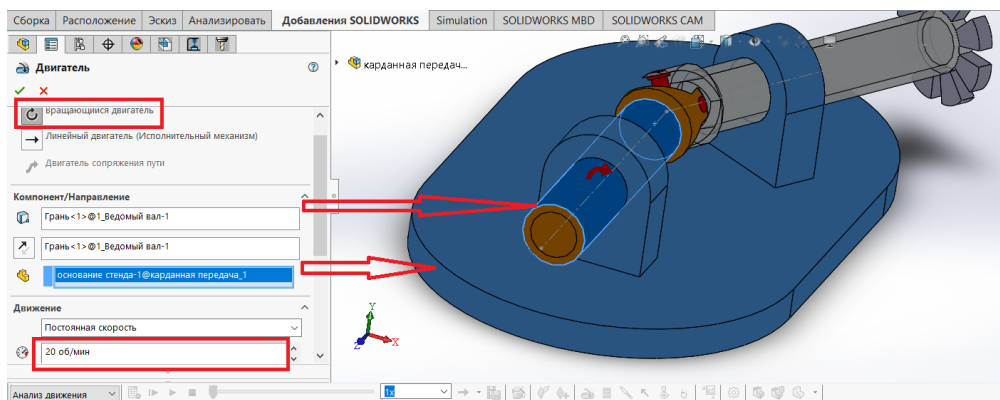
Назначение двигателя на ведущий вал карданной передачи
